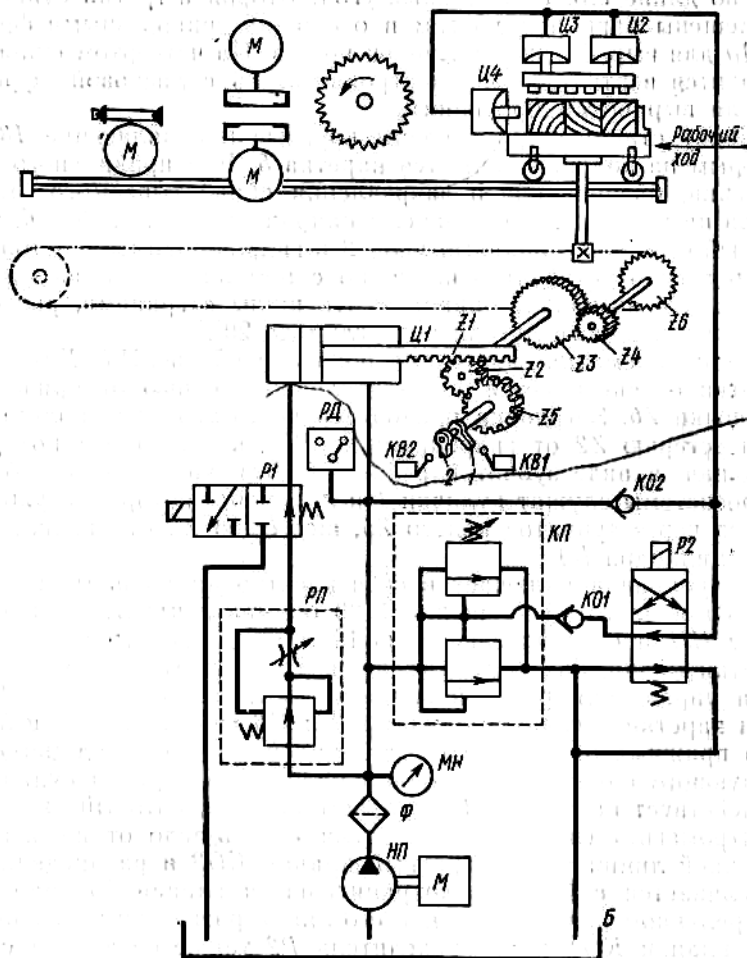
Гидрокинематическая схема одностороннего шипорезного станка для рамных шипов ШО16-4: 1, 2 — кулачки; НП — насос пластинчатый, Ф — фильтр, МИ — манометр, РП — регулятор потока, Р1, Р2 — распределители, КП — гидроклапан, КО1, КО2 — клапаны обратные, РД — реле давления. Ц1, Ц2, Ц3, Ц4 — гидроцилиндры, Z6 — звездочка, Z1, Z2 — реечная передача, Z3, Z4 — зубчатая передача, КВ1, КВ2 — конечные выключатели
